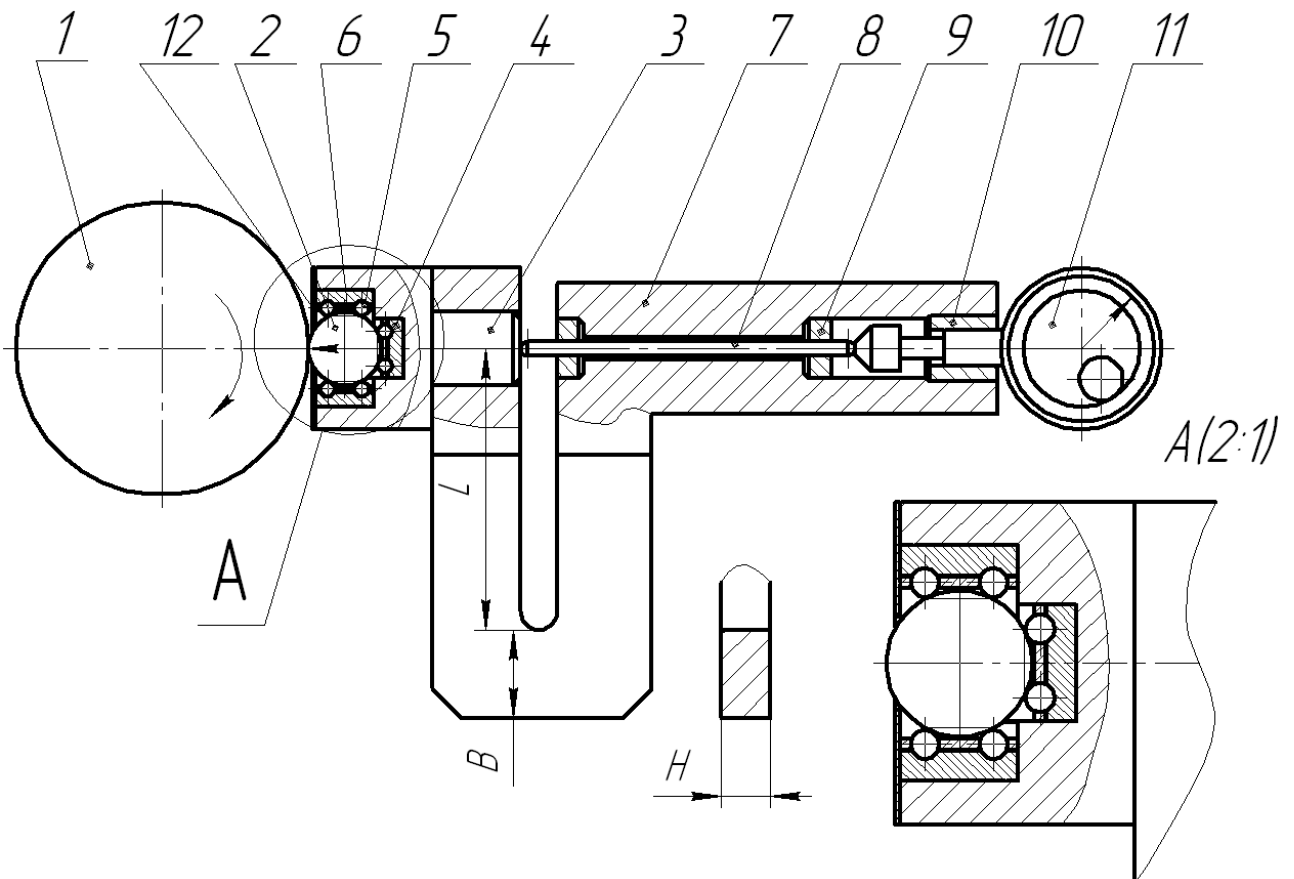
Конструкція спеціального інструменту для вигладжування поверхонь обертання
